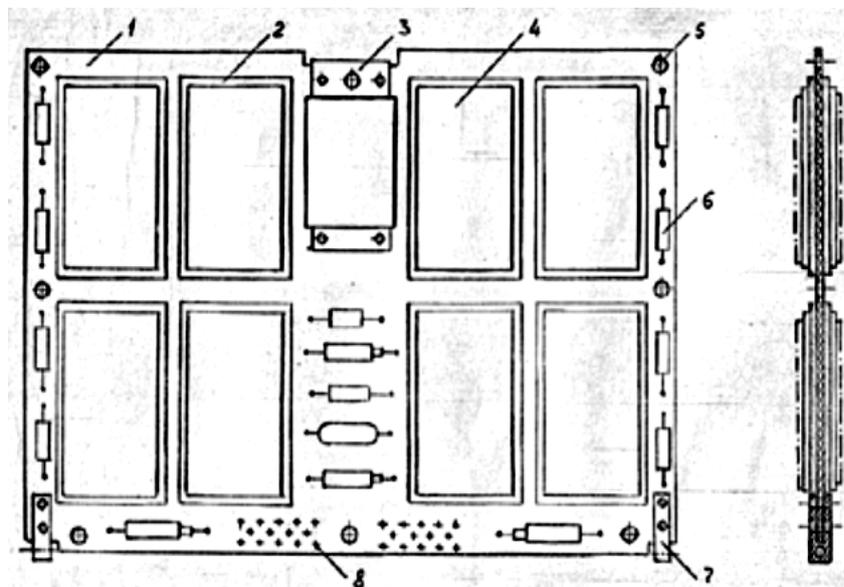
Ячейка герметичного блока МЭА книжной конструкции: 1 - печатная плата; 2 - индивидуальная металлическая шина; 3 - планка для стяжки ФЯ; 4 - МСБ; 5 - отверстие для крепления ФЯ; 6 - дискретный ЭРЭ; 7 - шарнир; 8 - зона межъячейной коммутации
